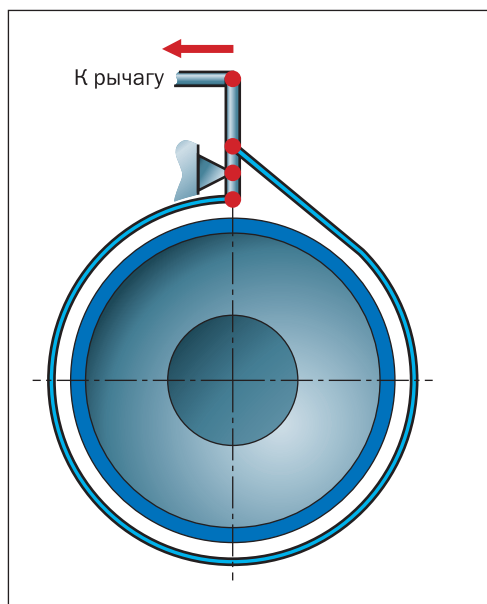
Ленточный барабанный тормозной механизм
